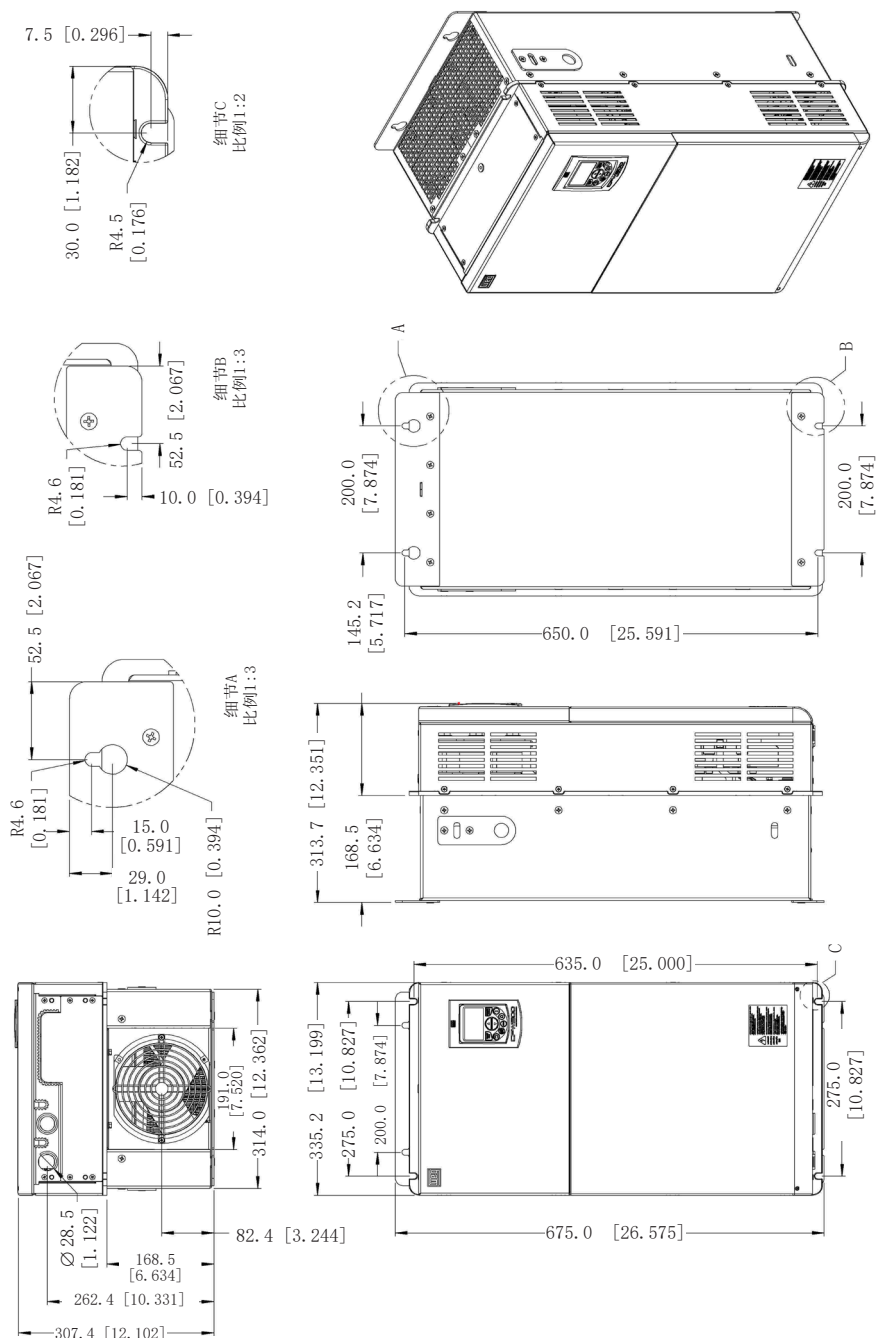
变频器尺寸 - 帧尺寸E - mm [in]
